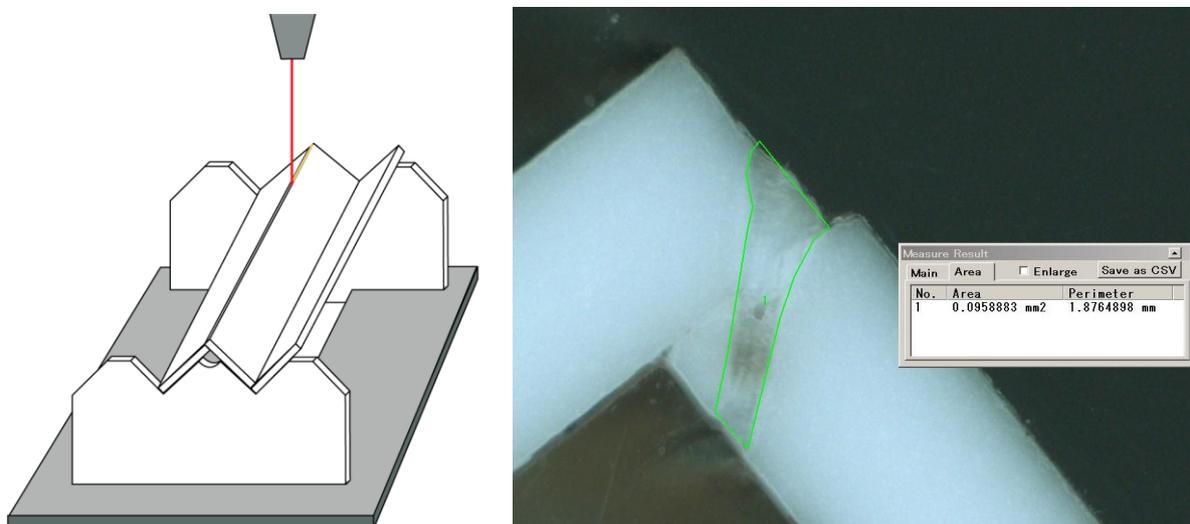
links: Halterung zur Schweißung einer Winkelgeometrie mit einer Nahtlänge von 30 mm; rechts: Schweißnaht (Laserleistung 1000 W, Scangeschwindigkeit 5 m/min)
